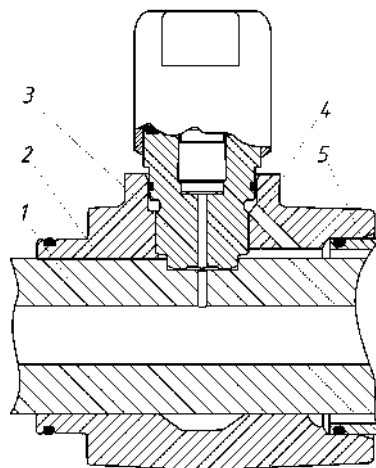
Фрагмент акумулятора тиску з зовнішнім бандажем для кріплення трубопроводів високого тиску: 1 - корпус акумулятора; 2 - бандаж; 3 - штуцер; 4 - дренажний канал збору протікання; 5 - зовнішній кожух акумулятора
